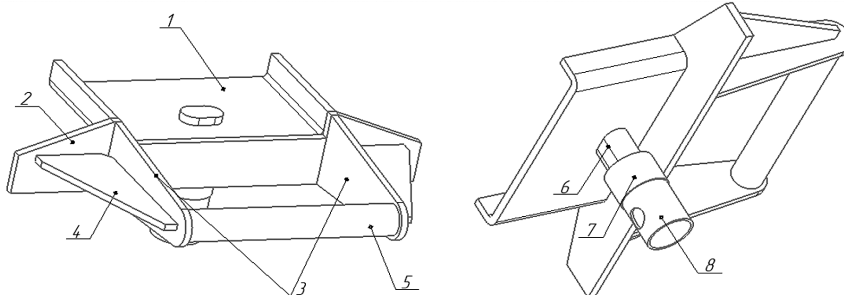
Съемный штанговый узел счалного устройства речного и берегового звена ПМП (ПМП-М): 1 — основание; 2 — упор; 3 — труба; 4 — кница; 5, 8 — труба; 6 — палец; 7 — гайка
